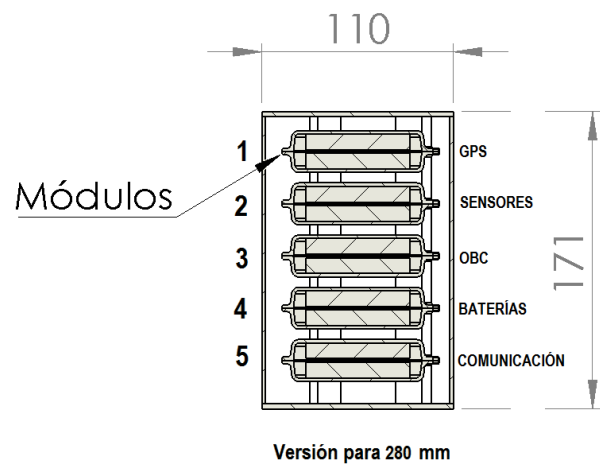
Versión de carga útil para motor cohete (Dimensiones en [mm]).
